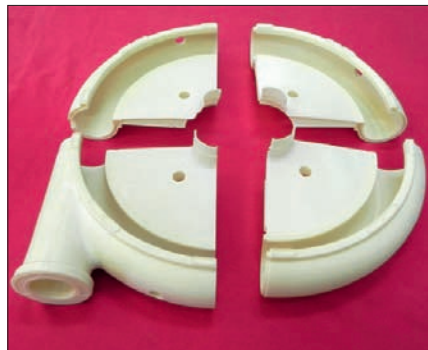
Модель улиточного корпуса, изготовленная из четырех частей
